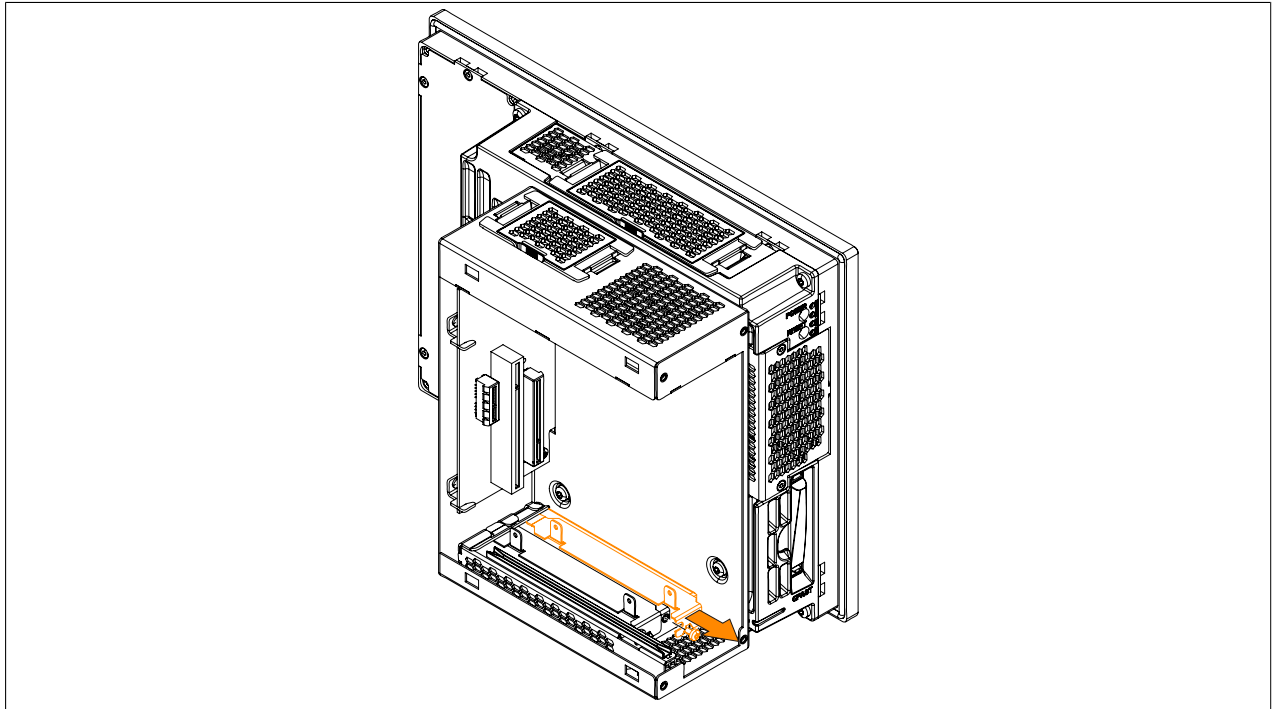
Torxschrauben lösen und Blindabdeckung entfernen
